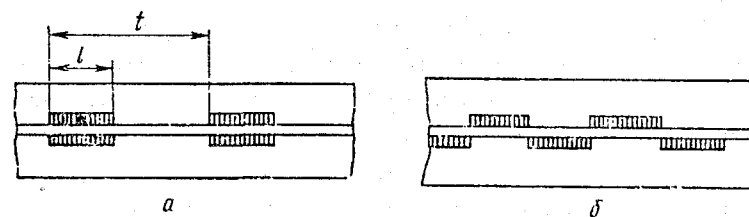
Прерывистые швы: а — цепной; б — шахматный; l — длина провариваемого участка; t — шаг шва
